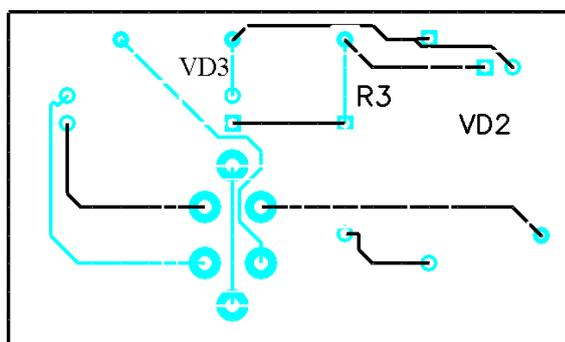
Окно редактора P-CAD PCB содержащего изображение ПП для схемы, изображенной на рис.20.
